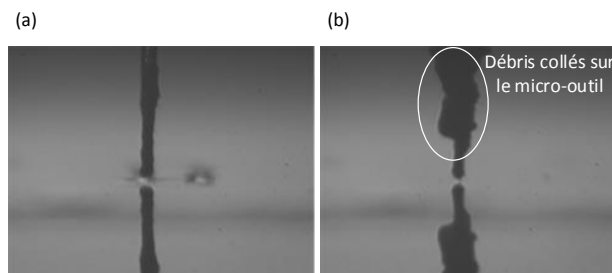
Outil avant (a) et après (b) un usinage montrant le collage de débris.
